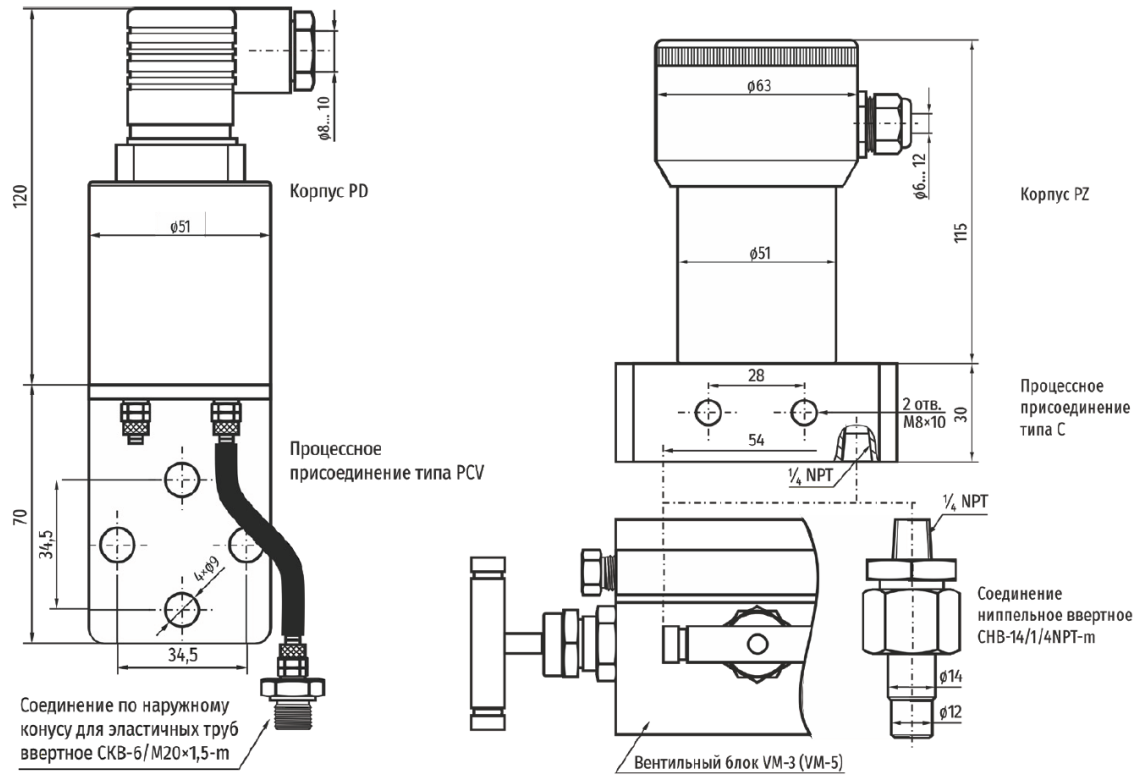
Преобразователь давления измерительный APR-2000G. Внешний вид и габаритные размеры
